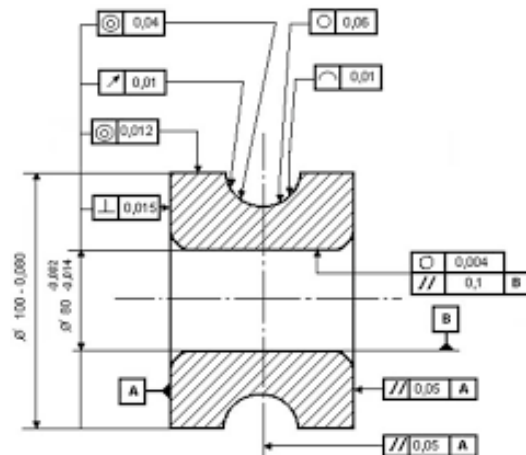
Ejemplo de tolerancias geométricas.
